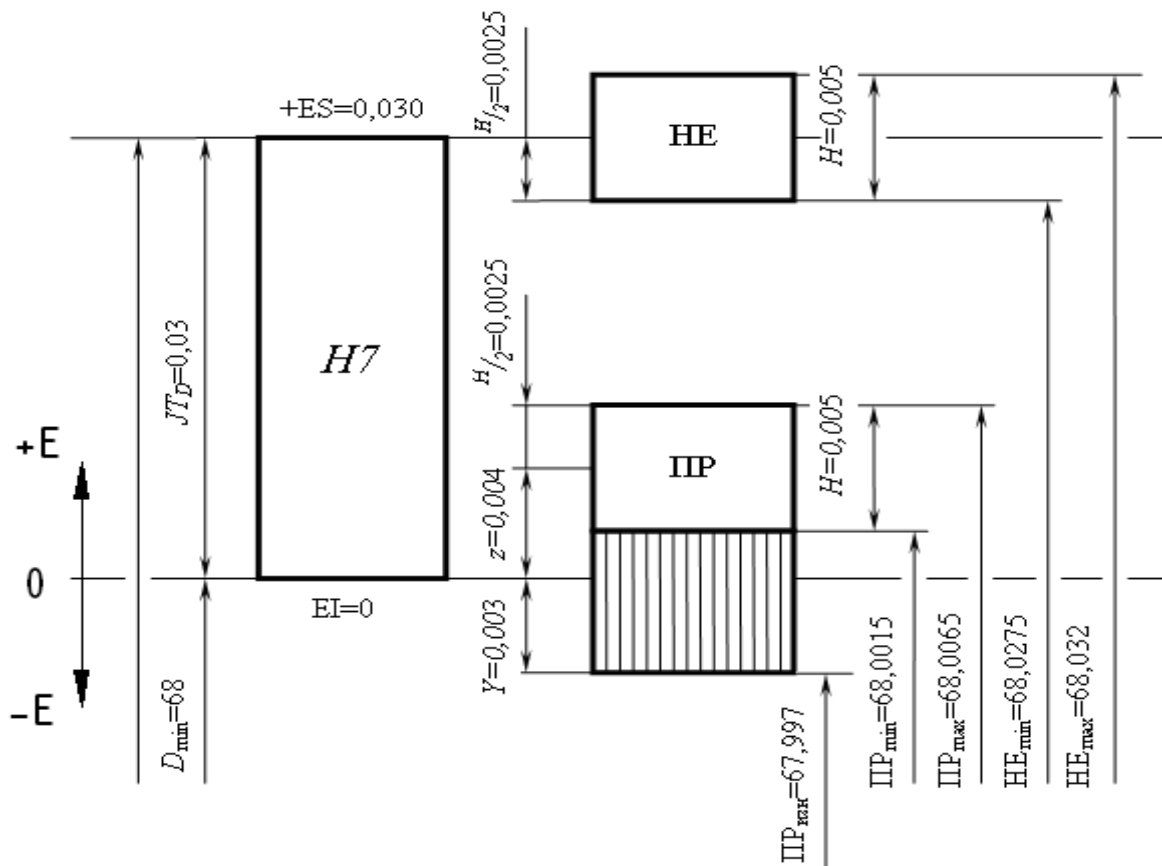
Схема расположения полей допусков отверстия и калибра-пробки
